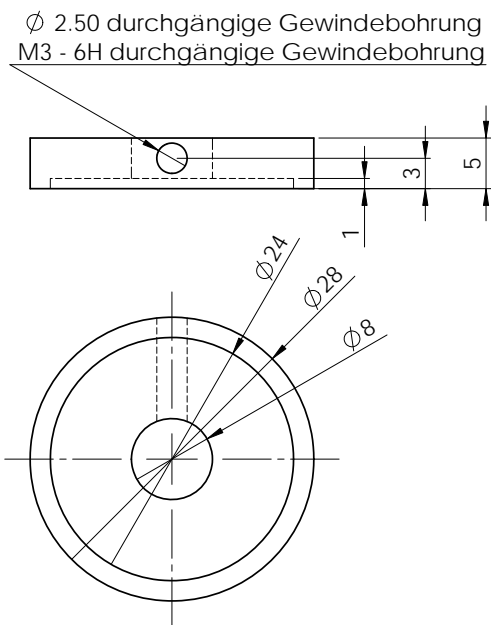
Technische Zeichnung des Strahlenschilds.
